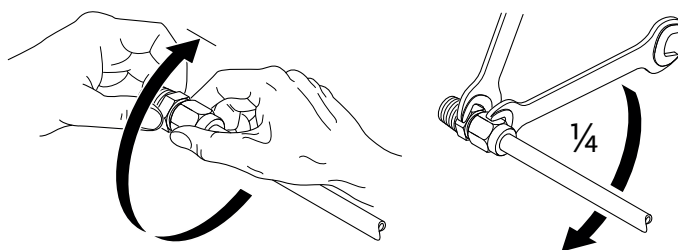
Дополнительный поворот резьбового соединения с обжимным кольцом на 1/4 оборота
